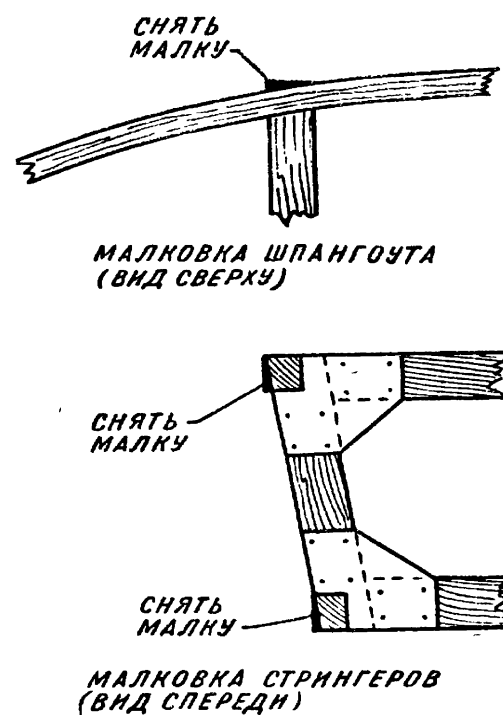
Малковка шпангоутов и стрингеров перед обшивкой корпуса фанерой
